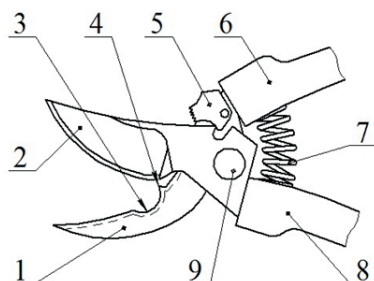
Конструктивная схема лезвийной пары секатора: 1 – противорежущий нож; 2 – режущий нож; 3 – вырез на лезвии противорежущего ножа; 4 – барьерное возвышение; 5 – замок; 6, 8 – рукоятки; 7 – пружина; 9 – шарнир
